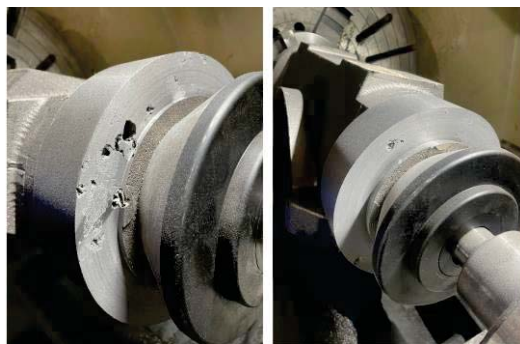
Дефекты на поверхности отливки после проведения механической обработки
